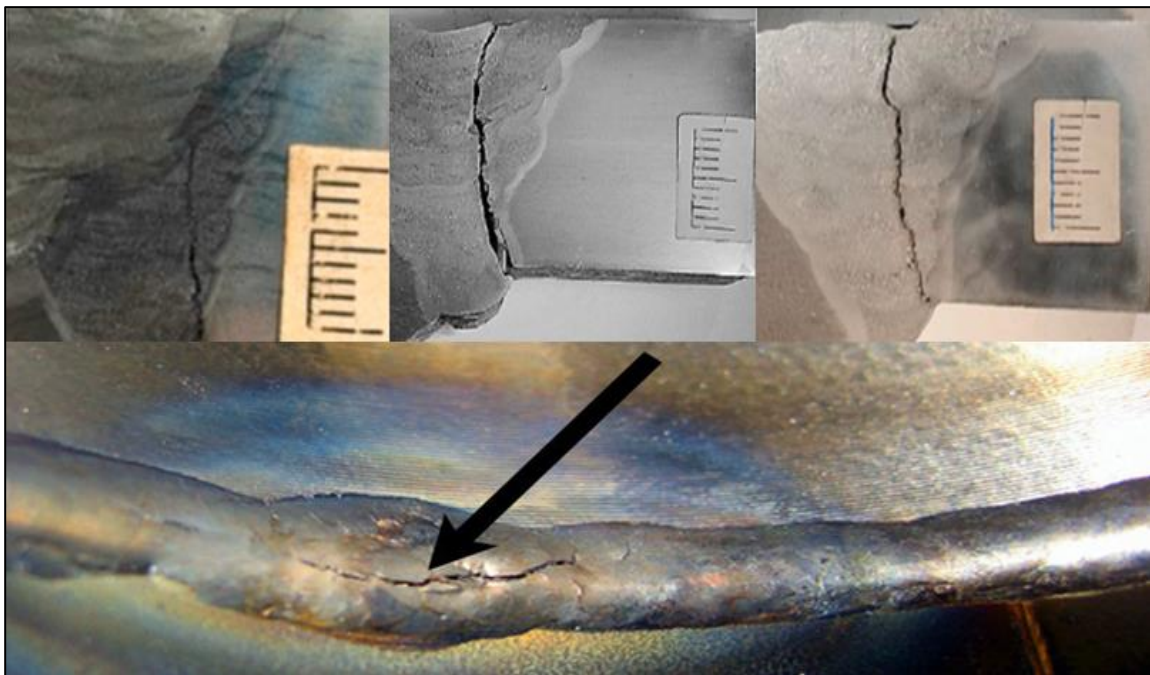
Grietas En Soldadura [50 y 51].
